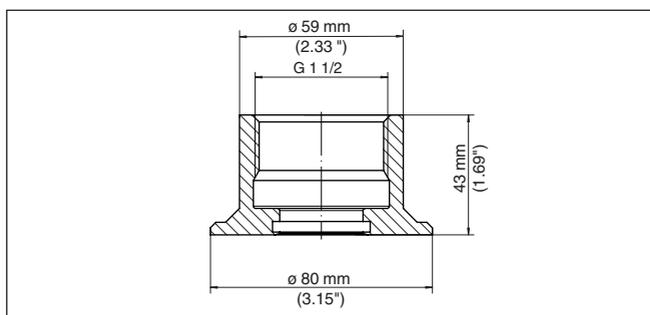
Medidas da luva para soldagem G1½ (DIN 3852-A)
